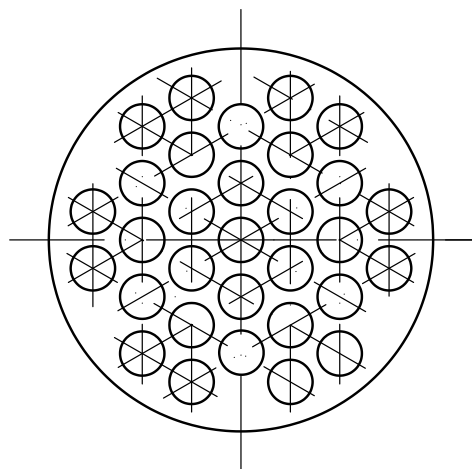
Схема расположения отверстий в закладной детали из припоя ПЖК-35 (без размеров)
